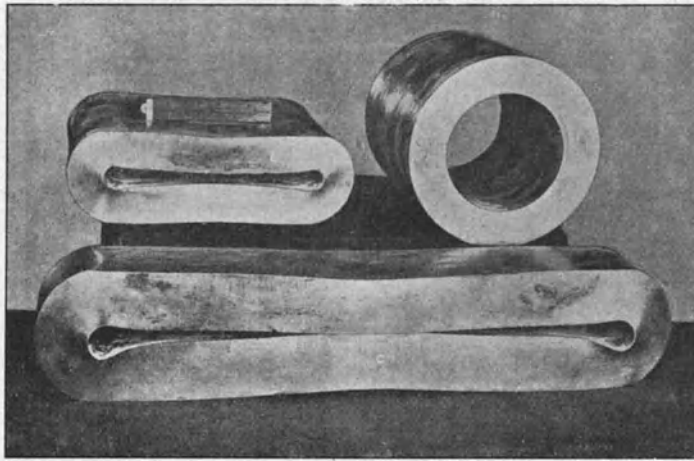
Geschützrohre aus weichem Bessemerstahl, unter dem Dampfhammer flachgeschlagen.
